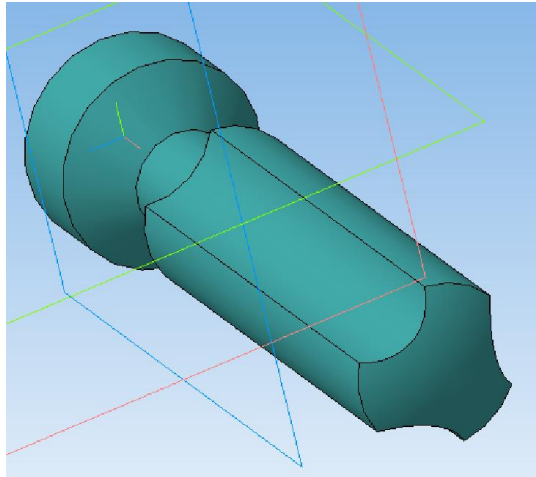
Пневмо аппарат клапанный, детализовка 3D сборки
